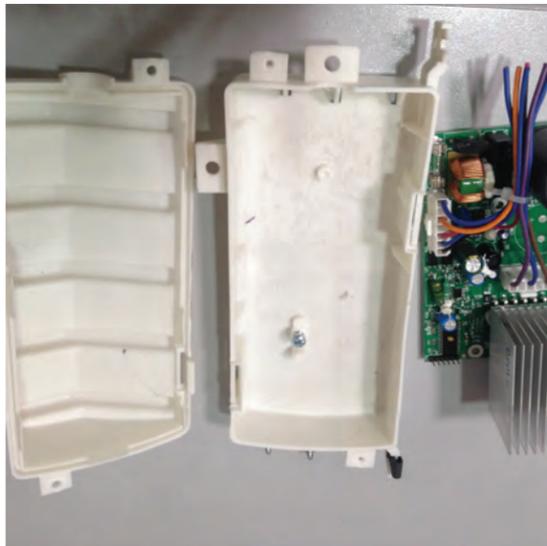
Conjunto driver board Sara Pro Fuente: Autoría propia
